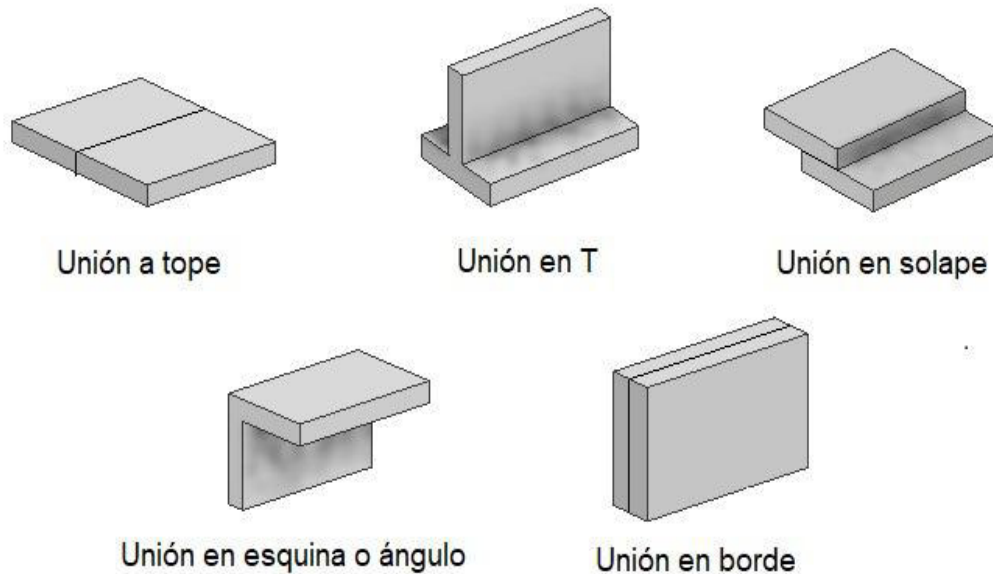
Diferentes tipos de uniones soldadas.
